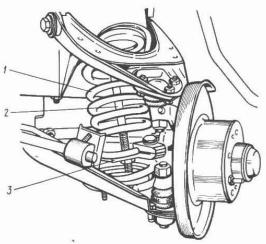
Desmontaje del muelle con el dispositivo 67.7828.9504:
